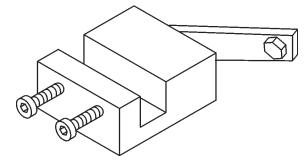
Outil de réglage des bras de la talocheuselisseuse
